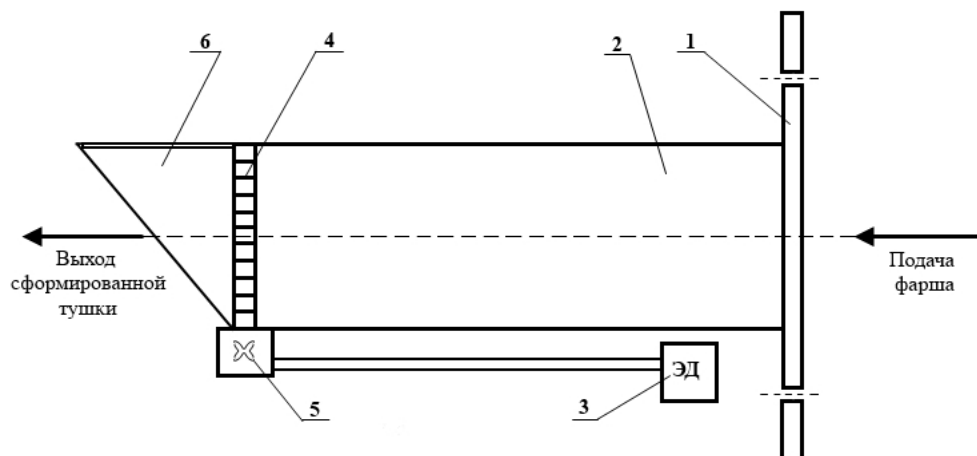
Насадочное устройство с ирисовой диафрагмой: 1 – фланец для крепления насадки к экструдеру; 2 – корпус насадочного устройства; 3 – автономный электропривод; 4 – ирисовая диафрагма; 5 – зубчатая передача; 6 – выходное отверстие
